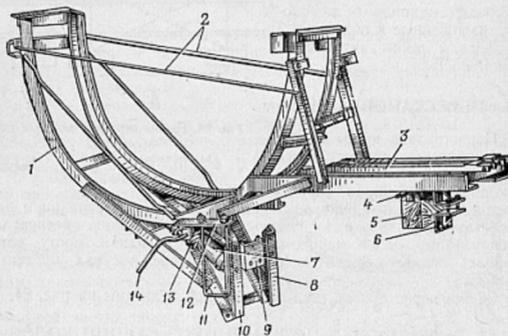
Вертикальный держатель запасного колеса автомобиля Урал-375Д:
